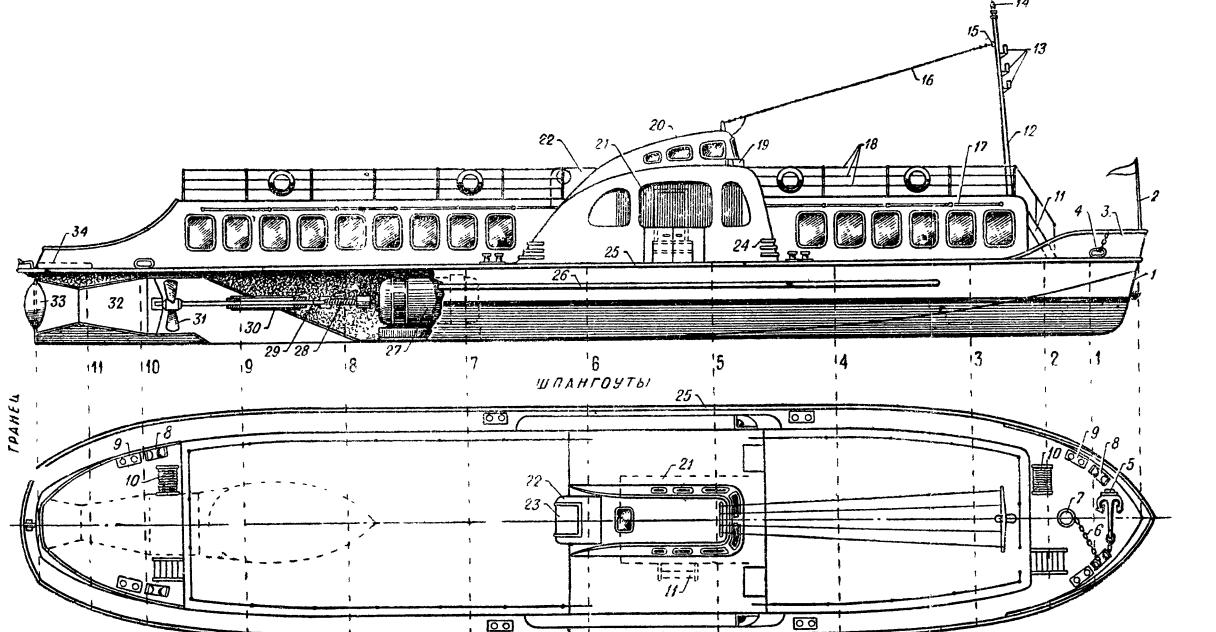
Вид модели сбоку и сверху: 1 — форштевень; 2 — флагшток; 3 — фальшборг; 4 — швартовые клюзы; 5 — якорь; 6 — якорная цепь; 7 — шпиль; 8 — кипонные пластины; 9 — кианты; 10 — вьюшки; 11 — трап; 12 — мачта; 13 — топовые огни; 14 — клотик; 15 — рей; 16 — антенна; 17 — поручни; 18 — леера; 19 —
